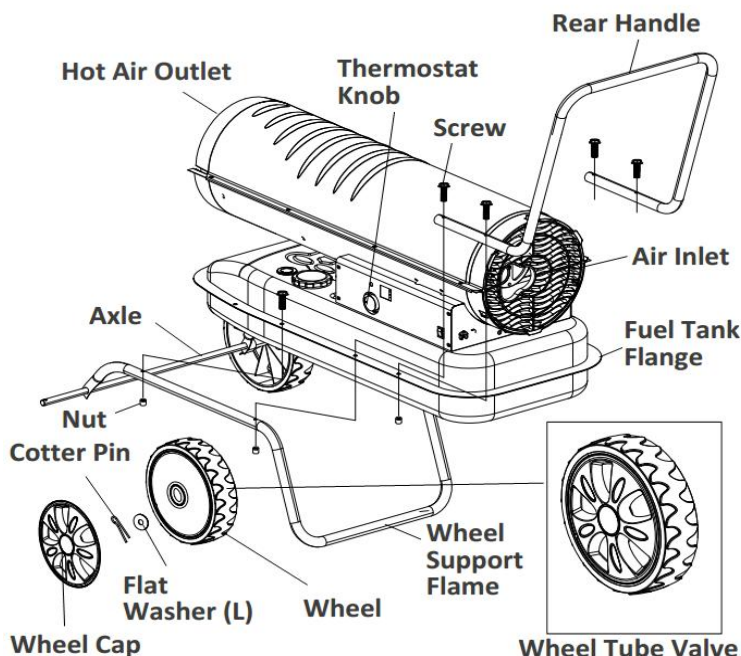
Assemblage des modèles ZB-K175/ZB-K215
